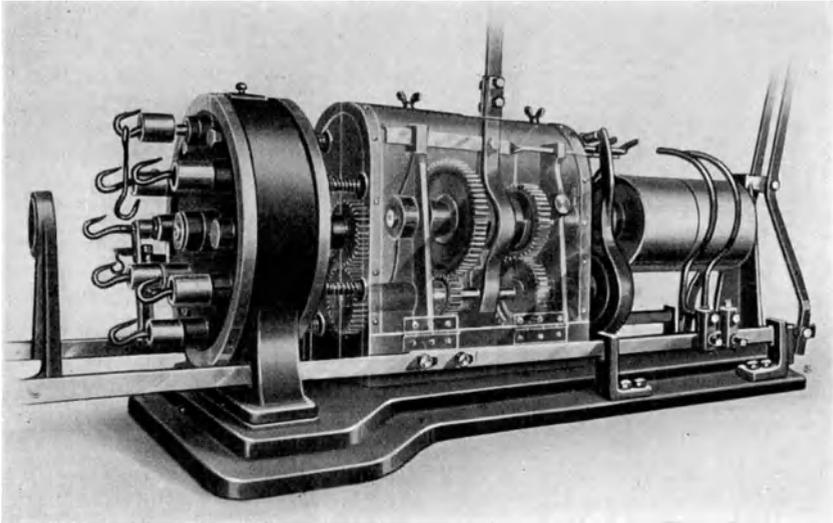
„Tomm“-Spinn-, Zwirn- und Schnürmaschine.
